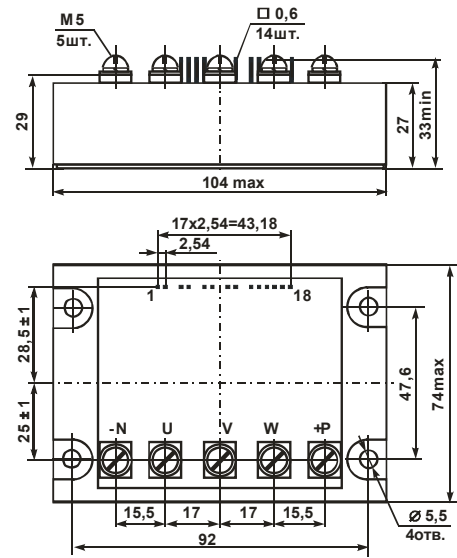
Габаритный чертеж модулей M13A-30(50,90)-6(12)
